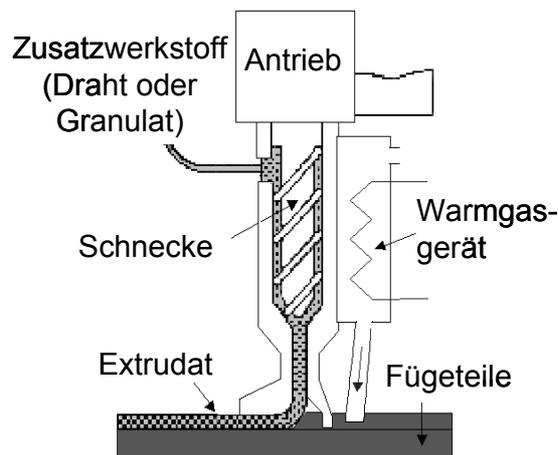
Extrusionsschweißen, schematisch. Fugenteile, Warmgasdüse Schweißschuh, Nahteinlauf
